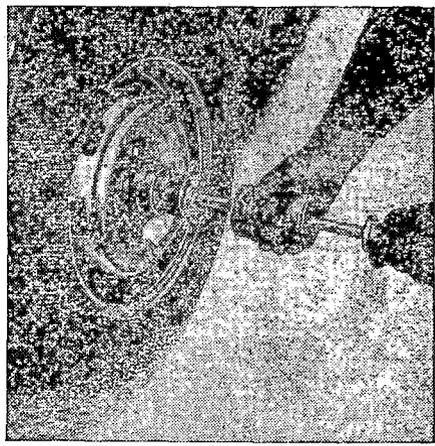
Выпрессовка колпачка ступицы переднего колеса ударным съемником 67.7801-9514.
